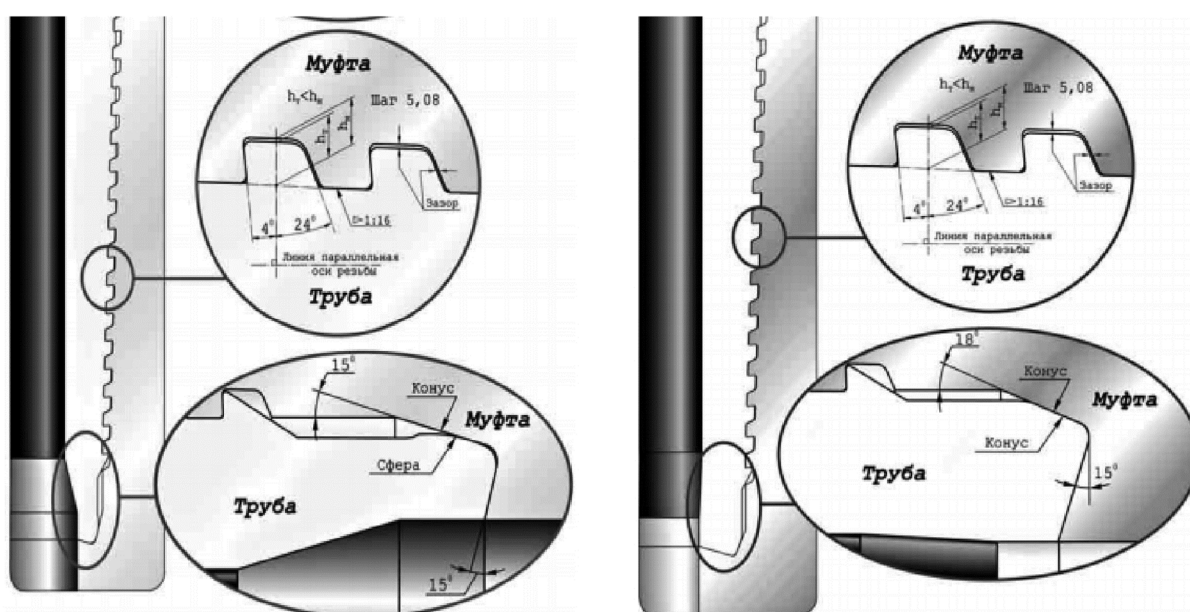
Примеры конструкций резьбовых соединений класса «Премиум»
